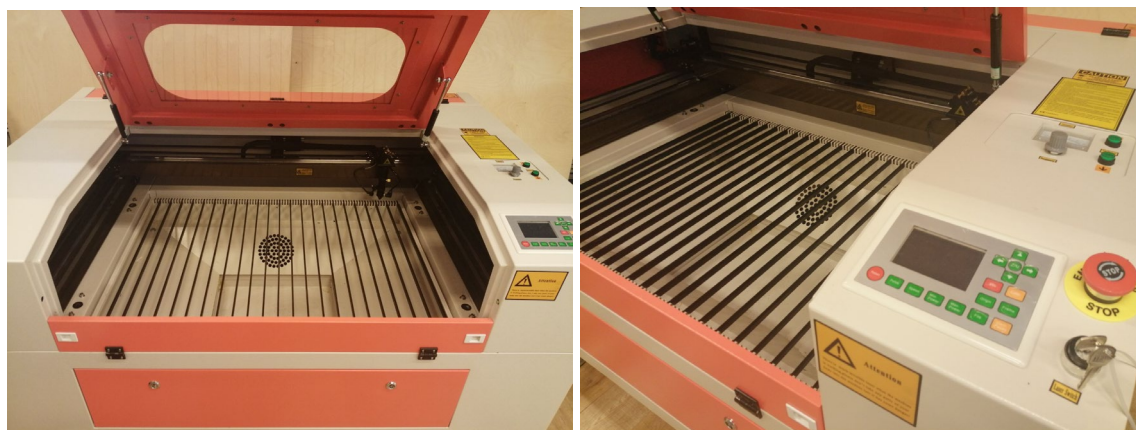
Комплексний лазерний верстат COMELZ CZ/M
